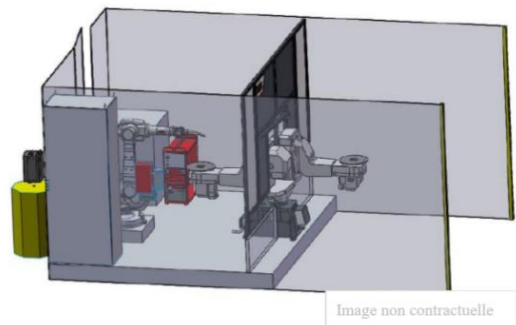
Aperçu de la proposition robot ABB de FTS Welding
